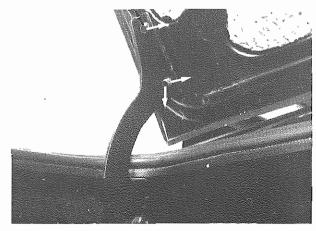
Viti fissaggio cofano Hood fixing screws
